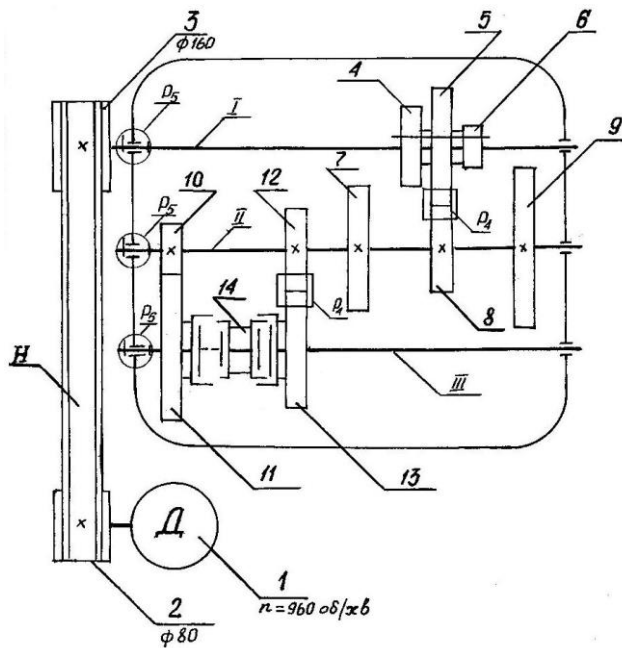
Кінематична схема коробки швидкостей токарного верстата
